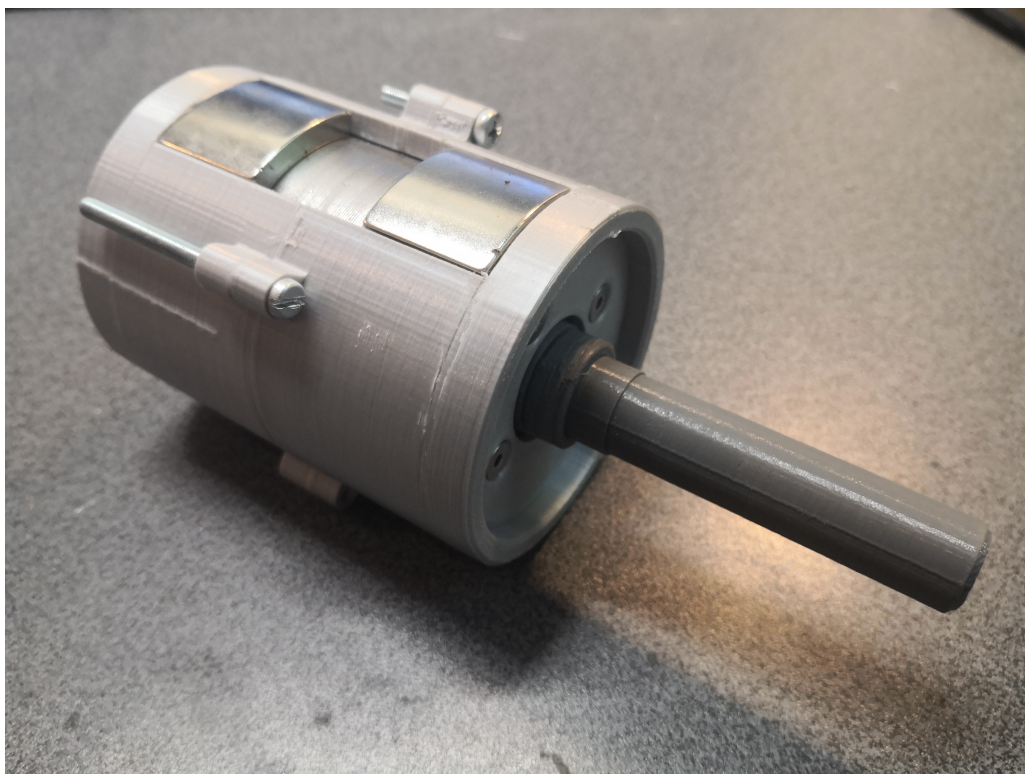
Rotor haute vitesse et son outil d'assemblage
